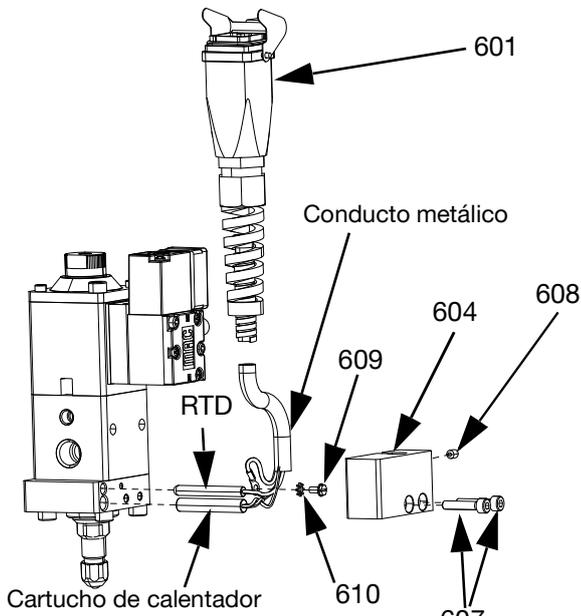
Conjunto de calentador para bloque de salida de 0 mm
